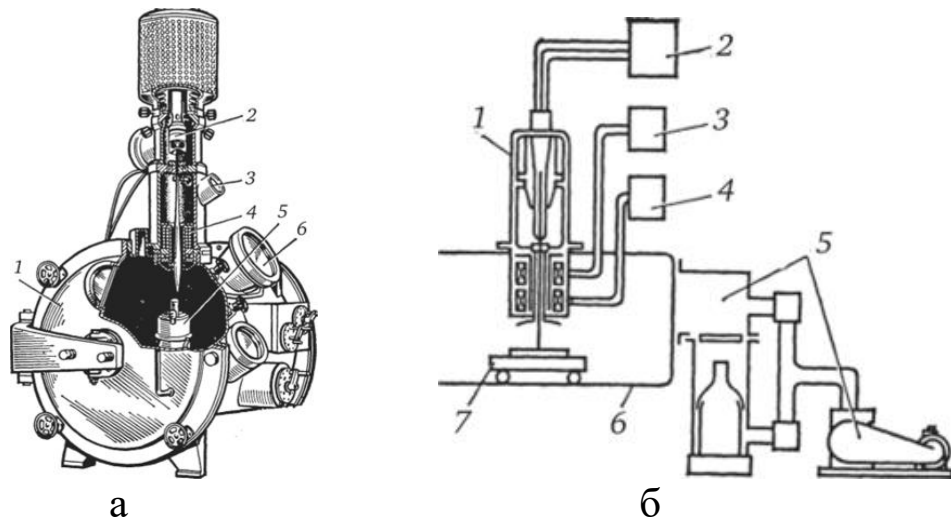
Установка для электронно-лучевой сварки
